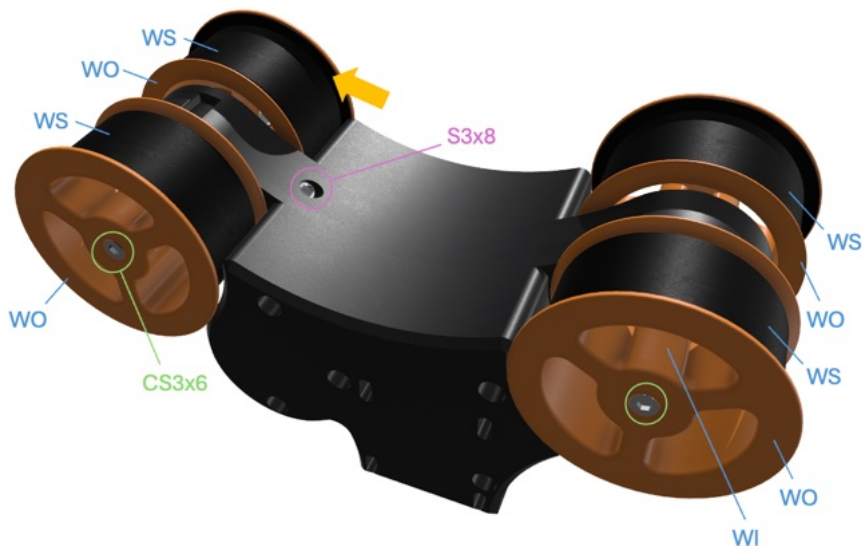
Rewinder-Chassis Montageschritt 29.
